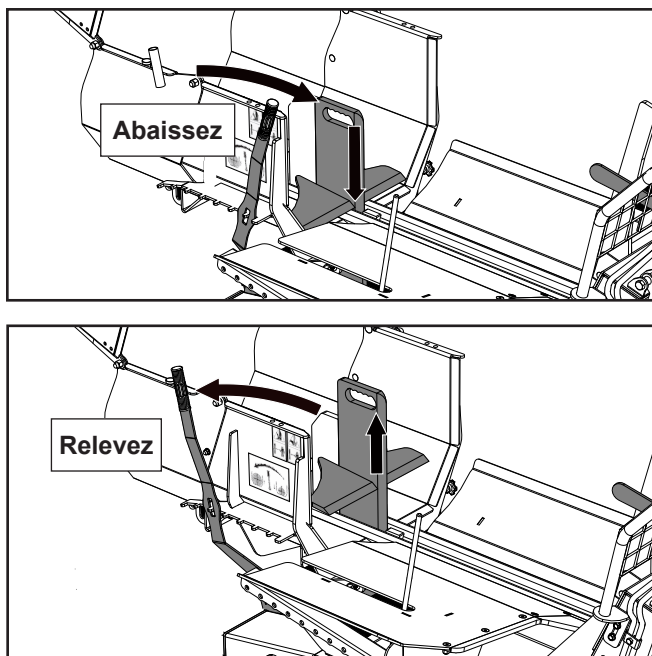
Levier d'ajustement de la hauteur du coin de fendage et étiquette
